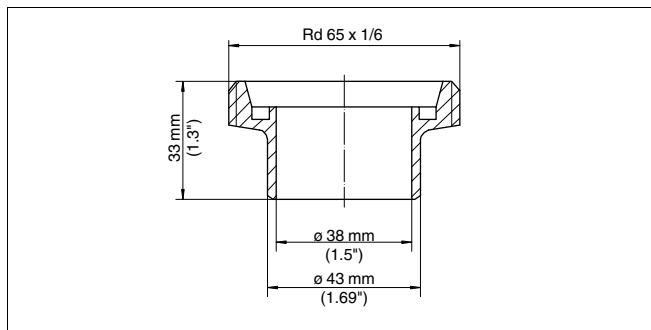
Размеры приварного штуцера - накидная гайка DN 40 по DIN 11851
